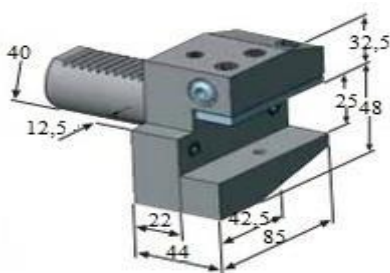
Резцедержатель DIN69880 форма B2
